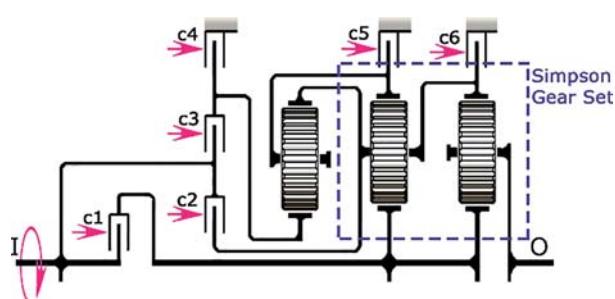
Кинематическая схема 5-ти ступенчатой планетарной коробки передач с тремя степенями свободы фирмы ZF Friedrichshafen:
